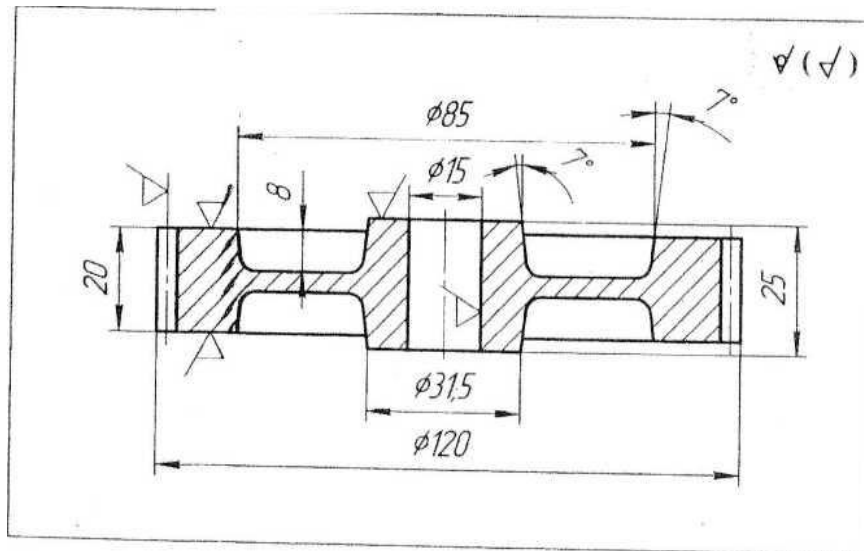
Зубчатое колесо, Сталь 30ХГТ.
